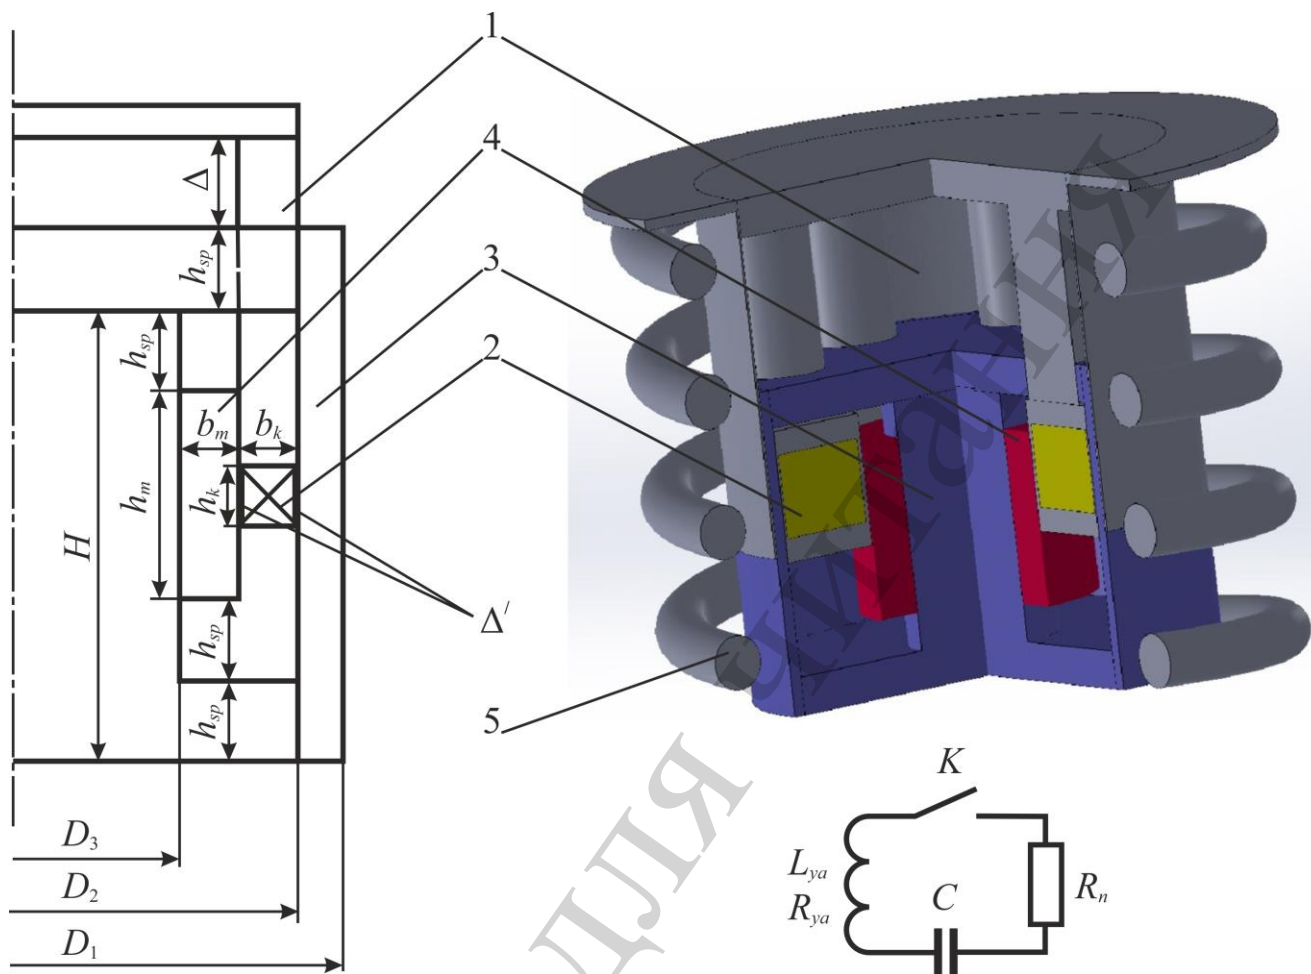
Електромеханічний амортизатор постійного струму: 1 – якор; 2 – обмотка якорю; 3 – станина; 4 – постійний магніт; 5 – пружина
